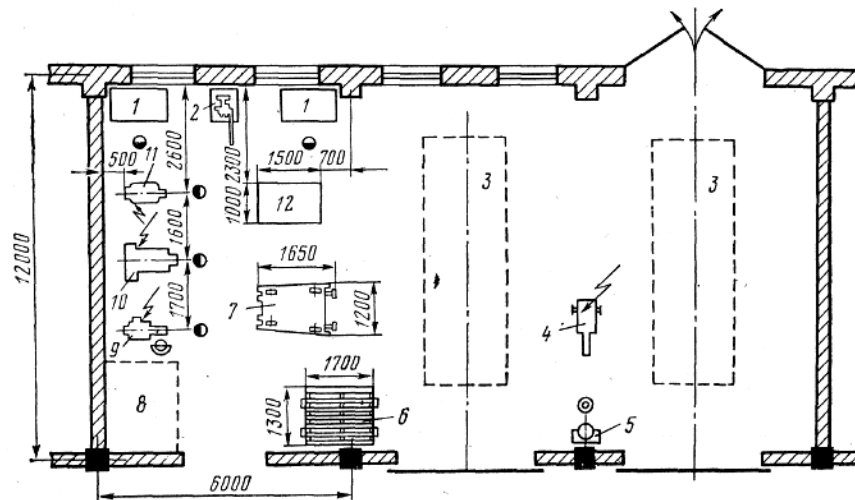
Зварювально -жестяницьке відділення ПАТ: 1 - верстак бляхаря; 2 - важільні ножиці; 3 - пост для зварювальних робіт; 4 - передвижний обдирно-шліфувальний верстат; 5 - штатив для балона з киснем; 6 - стелаж для крил; 7 - візок-стэнд для ремонту кабін; 8 - майданчик для листового матеріалу; 9 - апарат для точкового зварювання; 10 - зигмашина; 11 - вертикально-свердлувальний верстат; 12 - плита правильна
